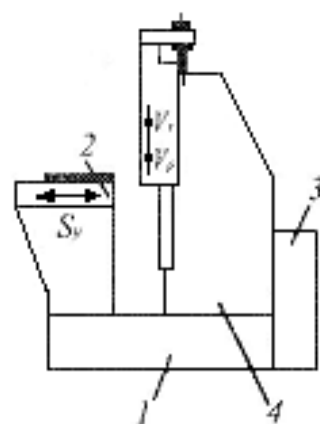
Загальний вигляд вертикально-протяжного верстата
